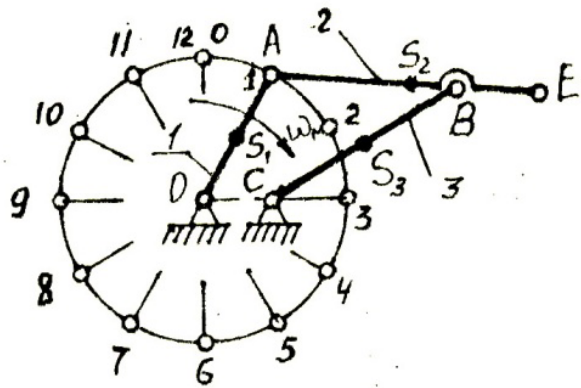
Схема 7 шарнирного четырехзвенника
